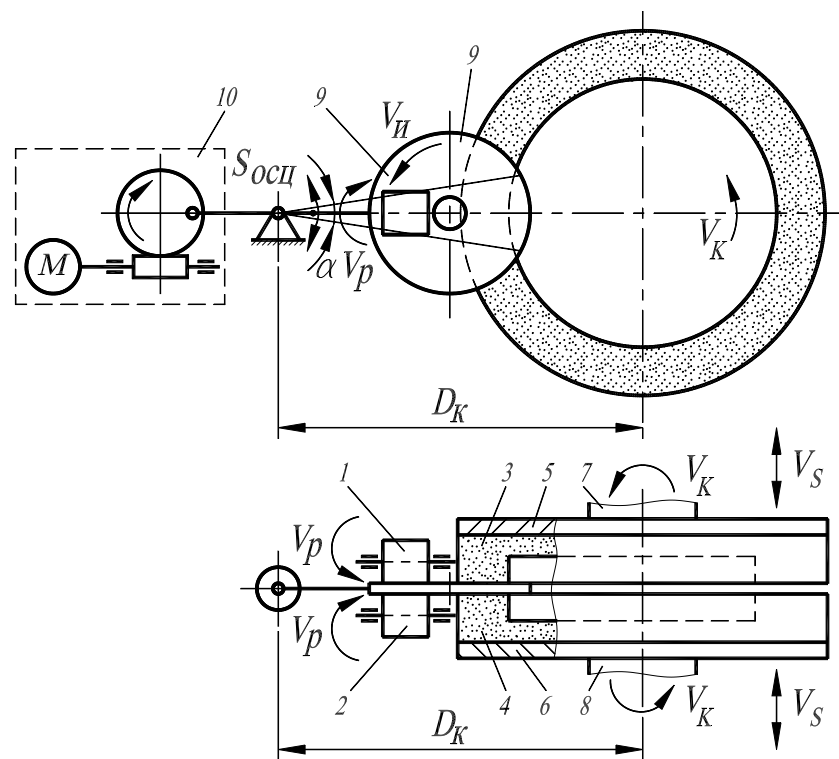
Способ двустороннего шлифования тонкостенных заготовок с качательной осцилляцией
